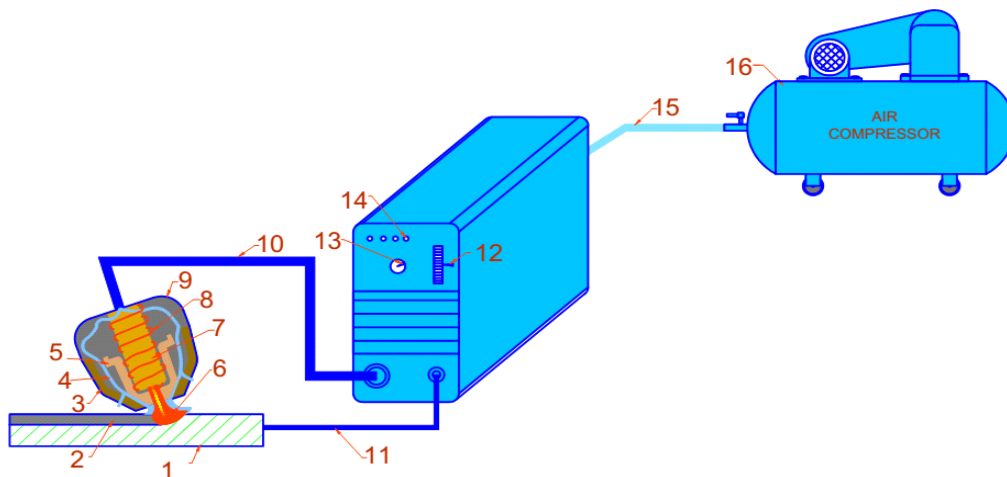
Schema de principiu a crăițuirii cu plasmă
